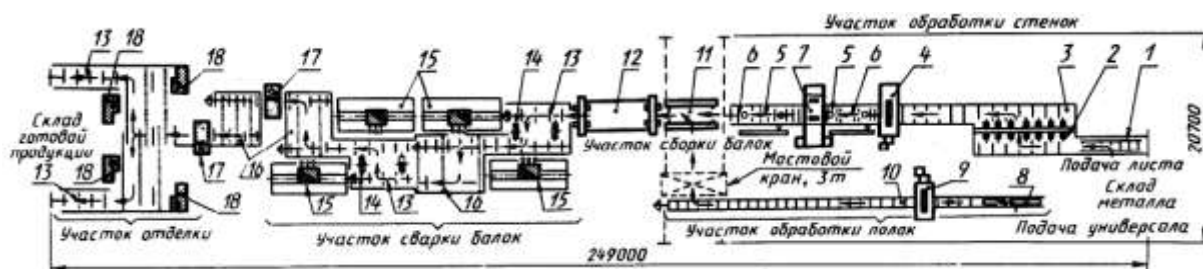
Схема поточной линии производства сварных двутавровых балок
